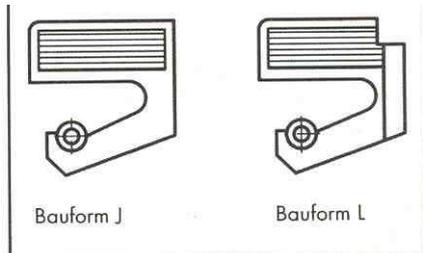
Gewebeverstärkte Ausführungen für große Durchmesser
